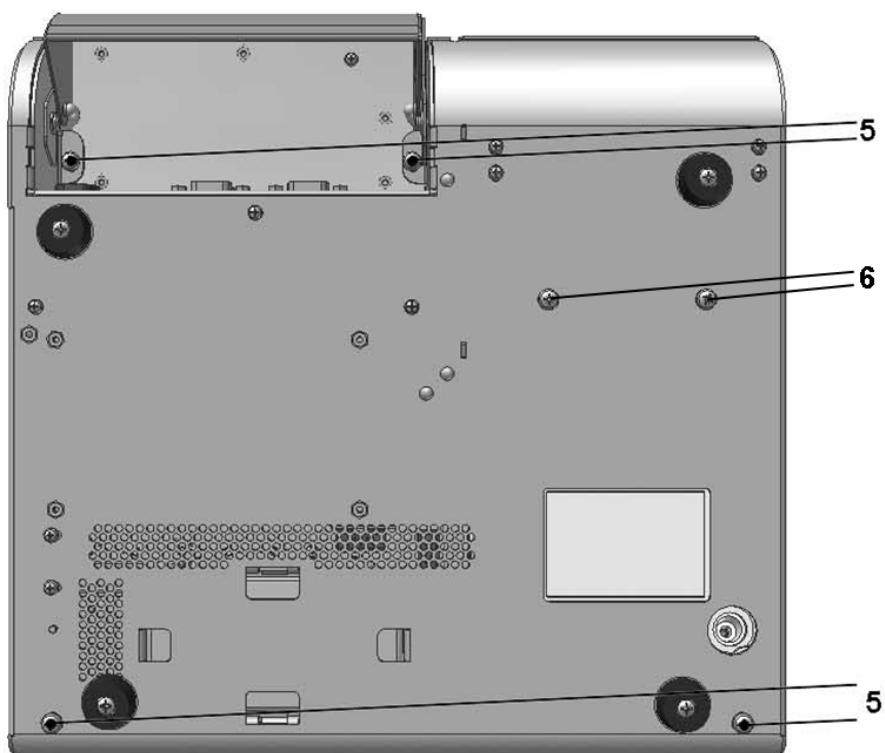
Винты крепления верхней части корпуса 5 и винты крепления ФР-а 6
